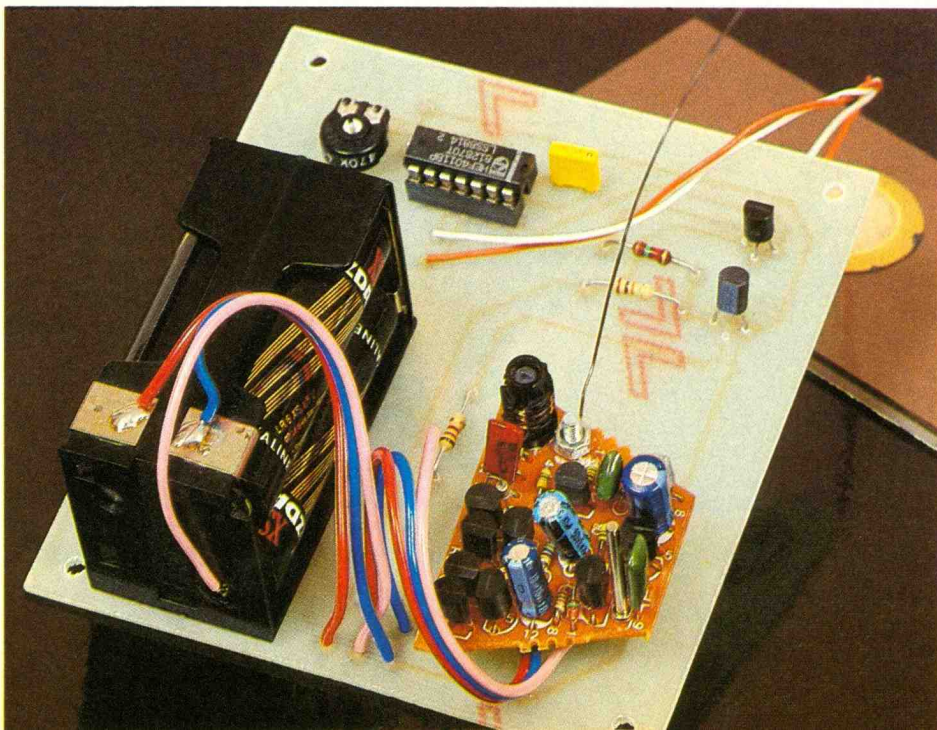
Gros plan sur le 4011 et son buzzer piezzo.
